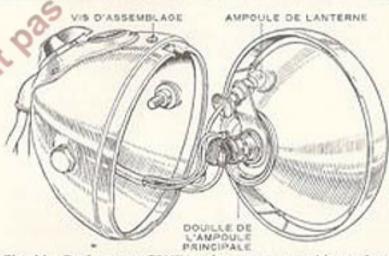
Projecteur "SSU" ancien avec ensemble optique et ampoule à baïonnette
